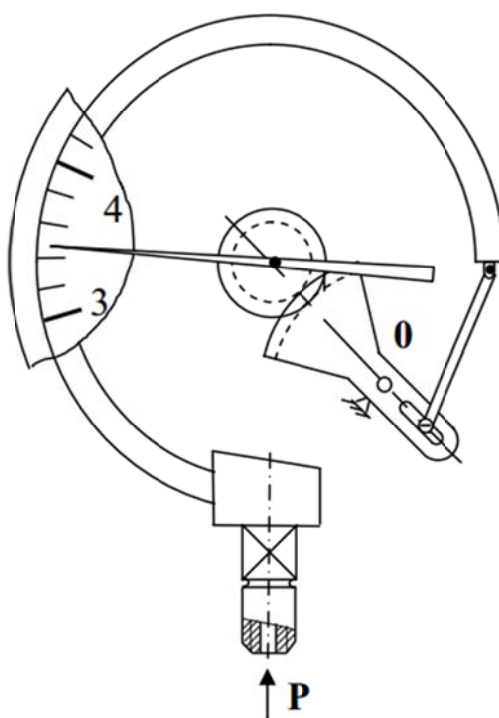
Конструкция манометра с одновитковой трубчатой пружиной
